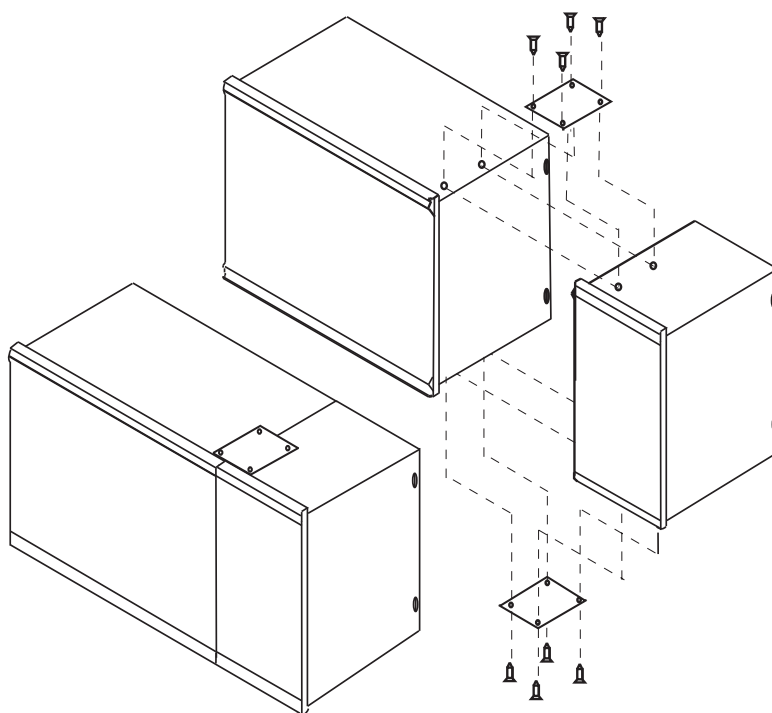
1 Einbaumontage und Einbaumontage mit Zwischenrahmen
